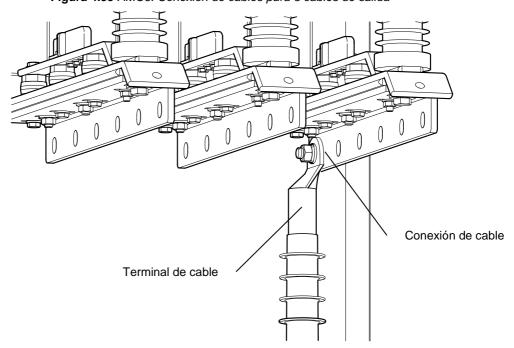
AMC9: Conexión de cables para 4, 5 y 6 cables de salida
